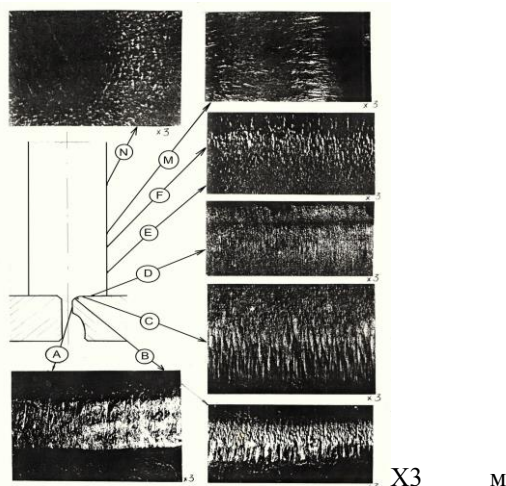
Характер пошкоджень поверхонь корпусу і бойка
